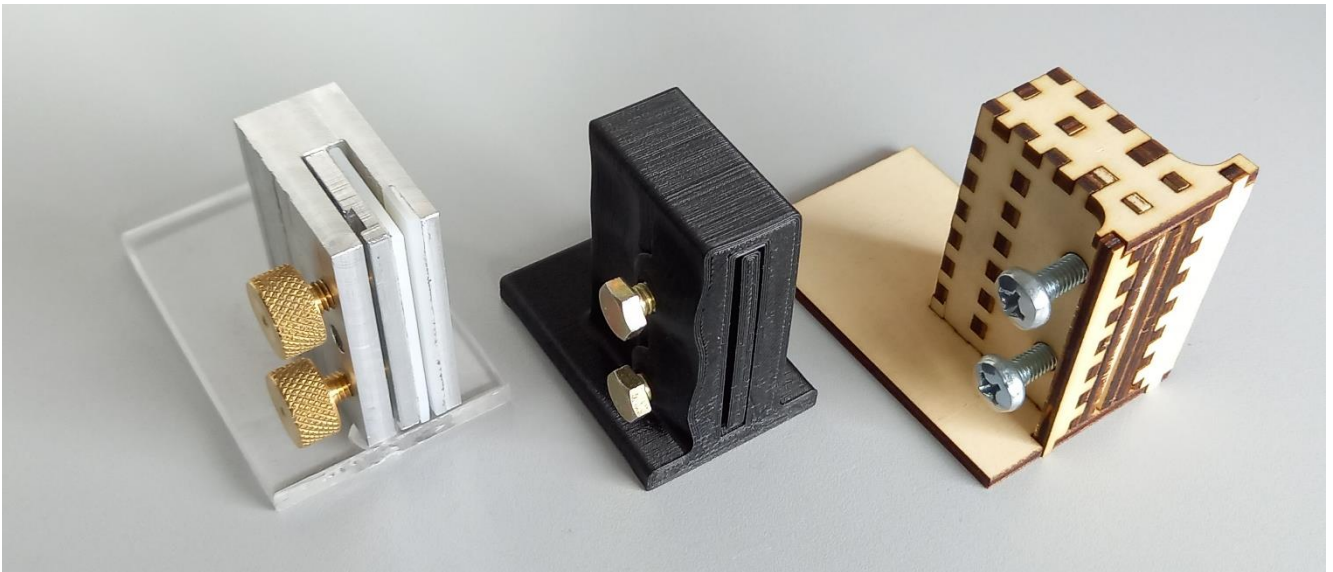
drei unterschiedliche Glashalter für die Prüfung; links: gefrästes Aluminium mit Klemmböcken aus Polyethylen und Fuß aus PMMA sowie gerändelten Klemmschrauben aus Messing; Mitte: in einem Stück ohne Nachbearbeitung 3D-gedruckter Halter mit eingesteckten Muttern (M6 flach) und Sechskantschrauben (M6) zum Klemmen des Glases; rechts: Lasergeschnittener Halter aus Sperrholz mit direkt ins Holz eingedrehten Schrauben zur Klemmung
